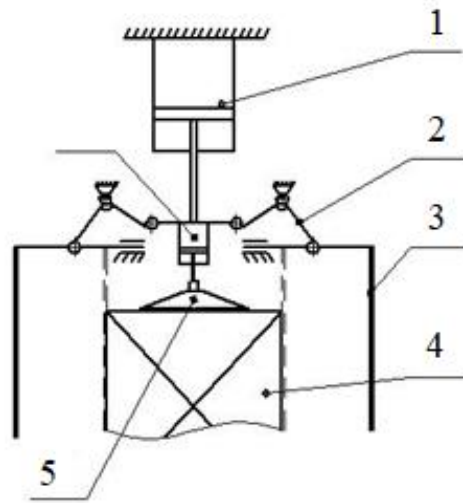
Схема комбінованого захоплювального пристрою механічно-вакуумного типу зі зворотно-поступальним рухом стулок: 1- пневмоциліндр; 2- важелі; 3- стулки; 4- упаковка; 5- вакуумний елемент
